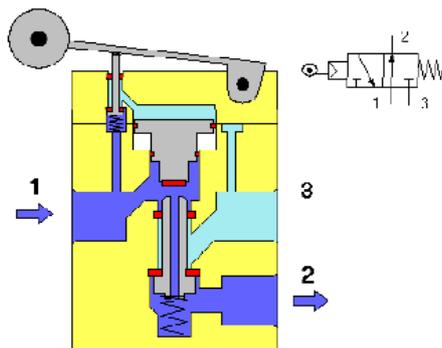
Válvula 3/2 inicialmente abierta accionada por rodillo
